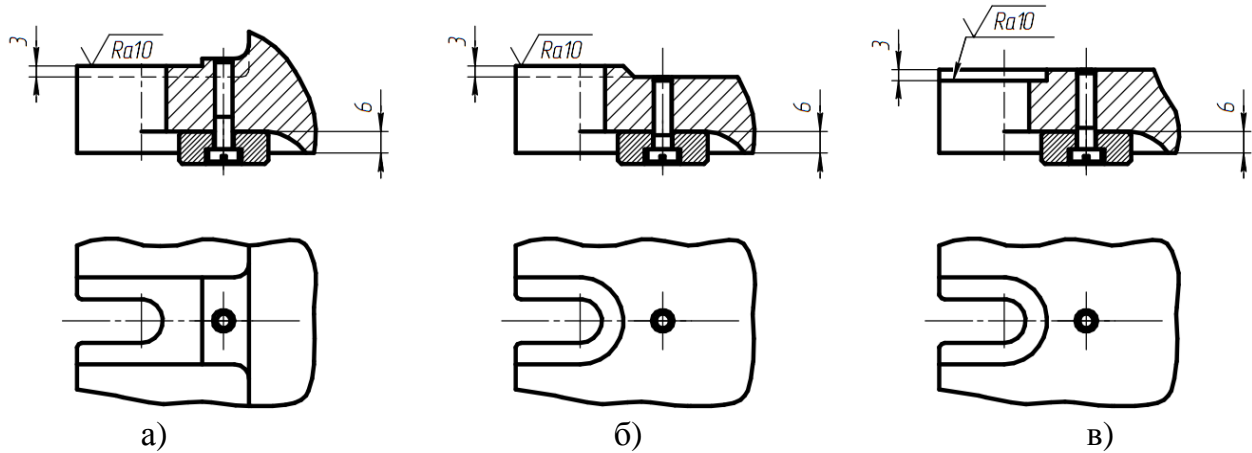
Конструкция проушин в корпусах приспособлений для литых (а) и (б) и прочих (в) корпусов
